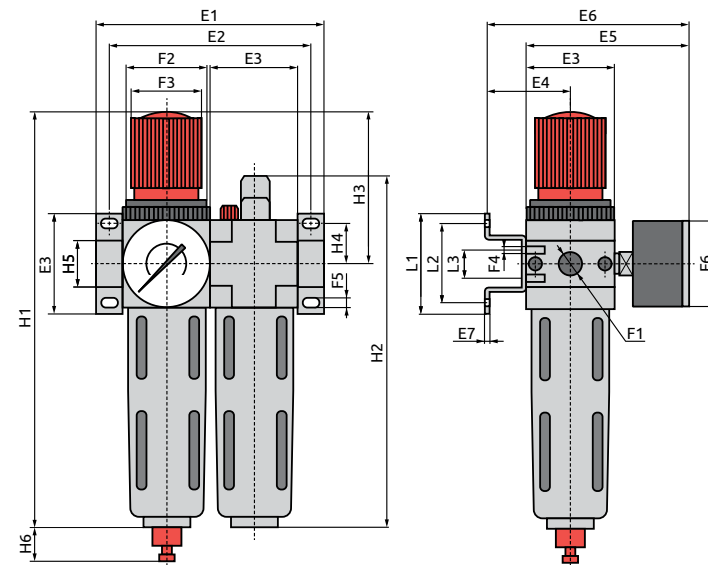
Габаритные размеры блоков подготовки сжатого воздуха ATU-FRL
